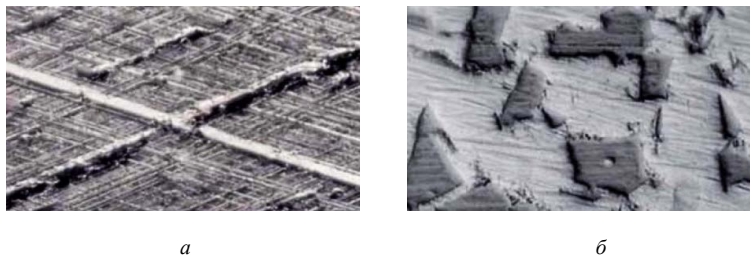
Внешний вид рабочей поверхности чугунных (а) и алюминиевых (б) цилиндров
